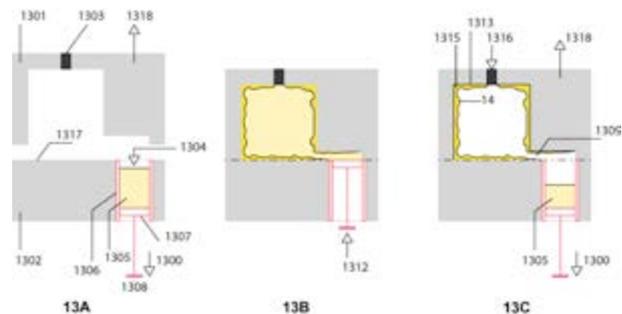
Coulée vidangée avec dispositif de type squeeze casting indirect et chambre d'injection thermorégulée
